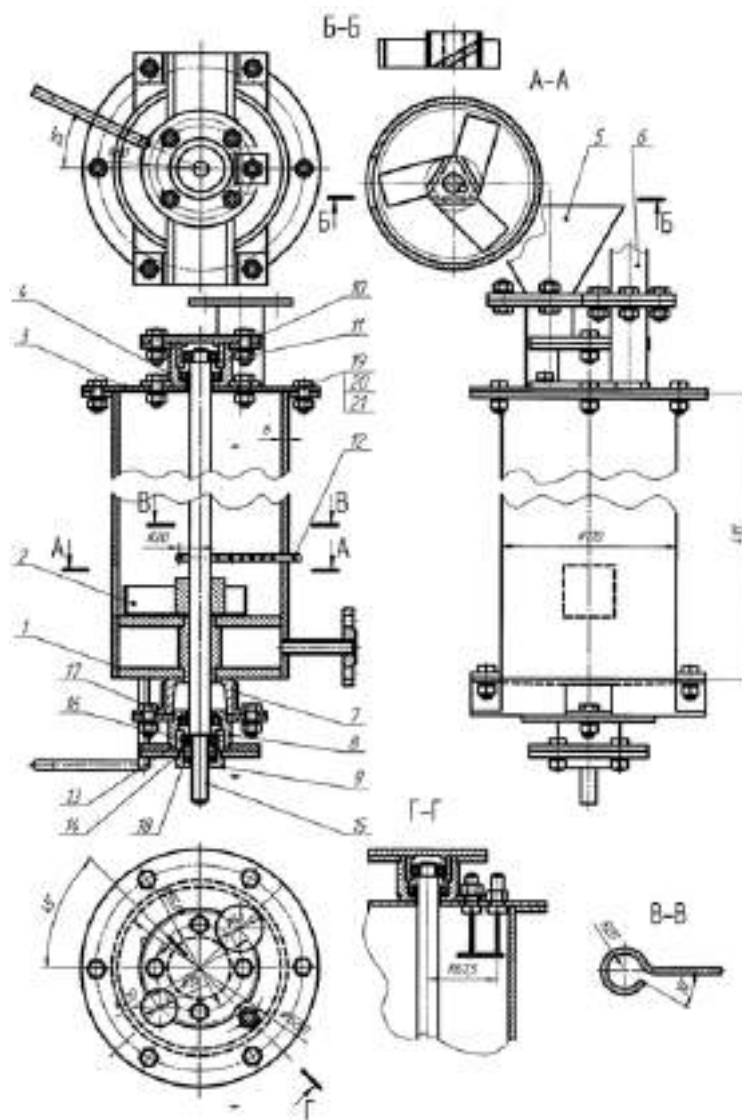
Робоче креслення лабораторної жаровні: 1 - корпус жаровні, 2 - ніж-мішалка, 3 - кришка жаровні, 4 - верхній корпус підшипника, 5 - приймальна воронка, 6 - витяжна труба, 7 - нижня опора, 8 - корпус підшипника, 9 - кришка підшипника, 10 - глуха кришка підшипника, 11 - підшипник, 12 - зволожувальна труба, 13 - ущільнення, 14 - підшипник, 15 - вал чана жаровні, 16 - опорна втулка, 17 - трубка для сходу конденсату, 18 - ущільнення підшипника, 19, 20, 21 – метизи
